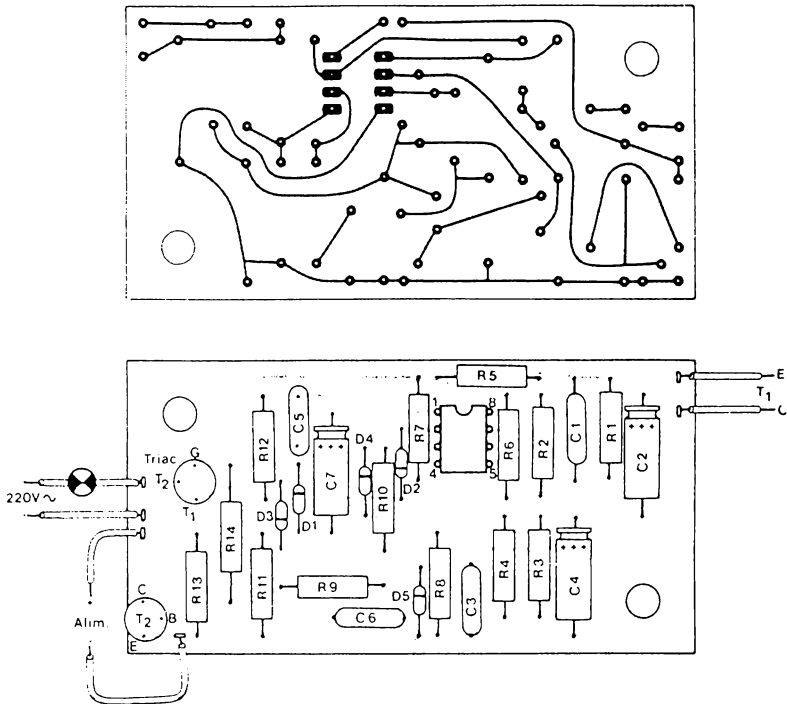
Circuit imprimé pour le récepteur de la figure 7 prévu pour composants d'assez grandes dimensions. La plaquette mesure 43 × 85 mm.
